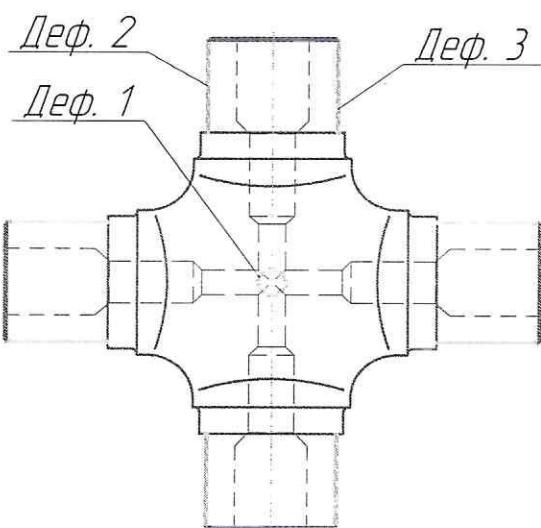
Крестовина карданного вала трактора К-700.
